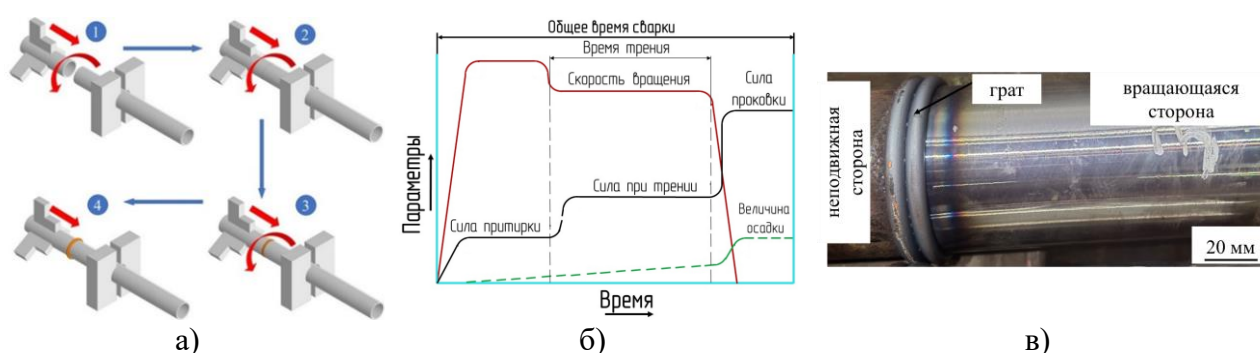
Ротационная сварка трением с непрерывным приводом:
